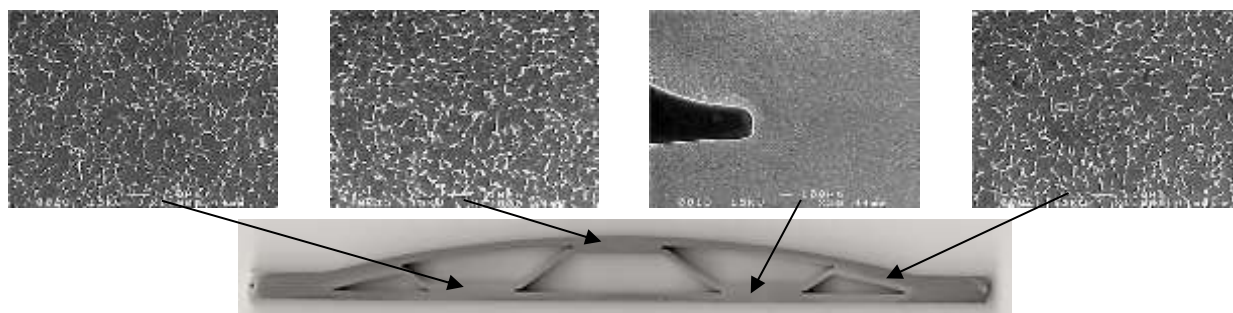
Микроструктура ТФС плоского образца полый лопатки из титанового сплава BT6.
